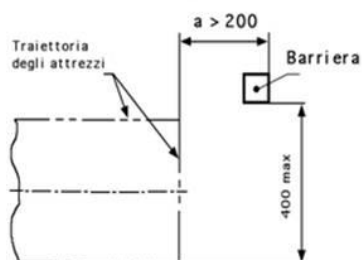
prospetto indicante le distanze di sicurezza delle barriere di protezione dalla traiettoria degli utensili - tratte dalla EN 708
